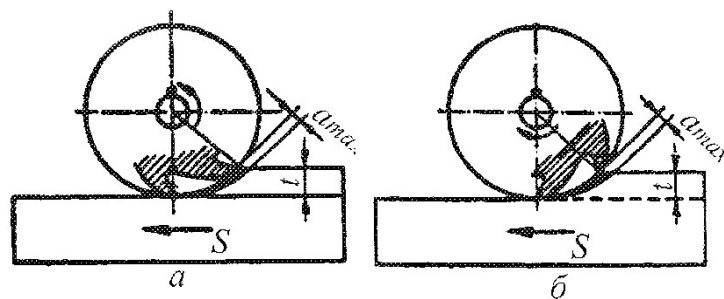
Схеми зустрічного (а) та попутного (б) фрезерування
